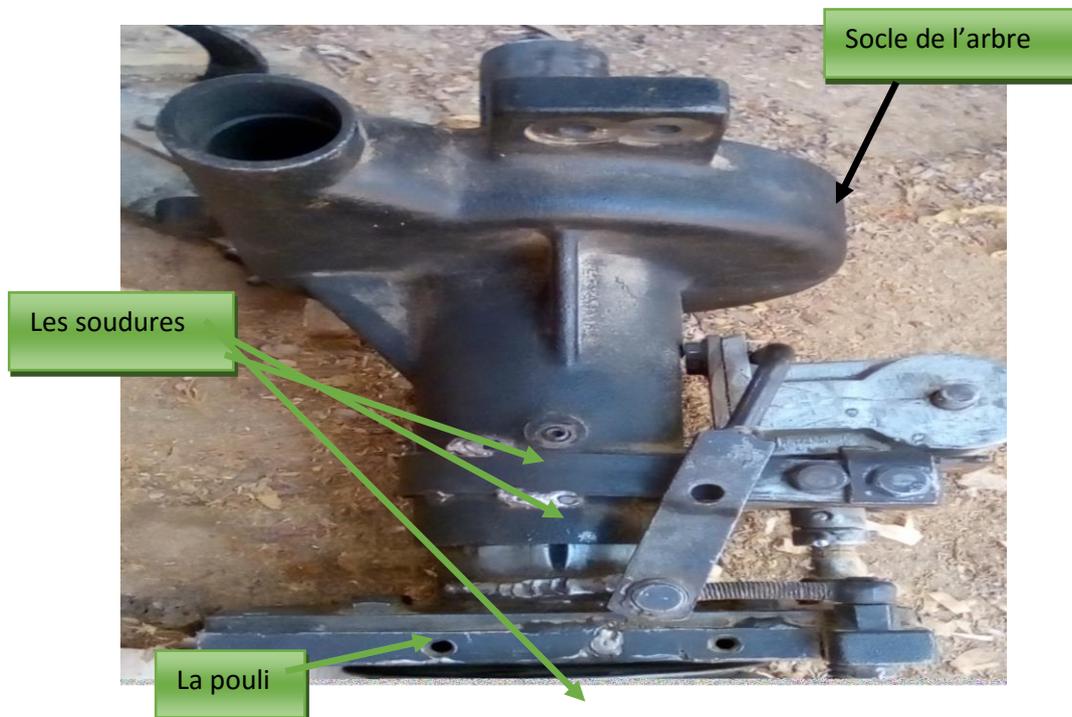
fréquence de soudure sur l'arbre porte outil de la toupie
